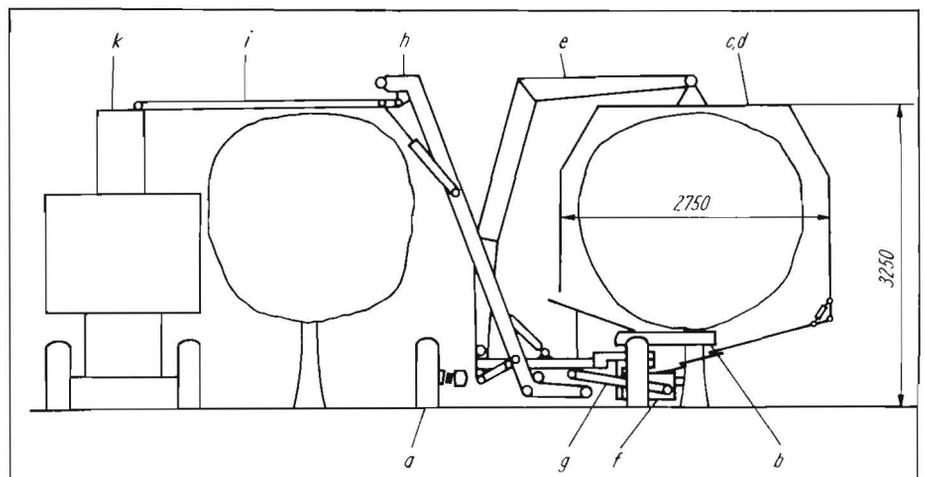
Draufsicht der Obsterntemaschine rabo 3500;
